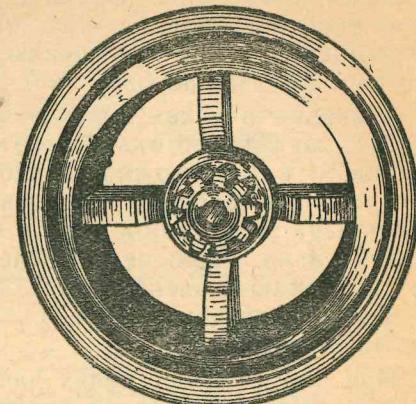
Схема устройства пневматической роторной сверлилки.
